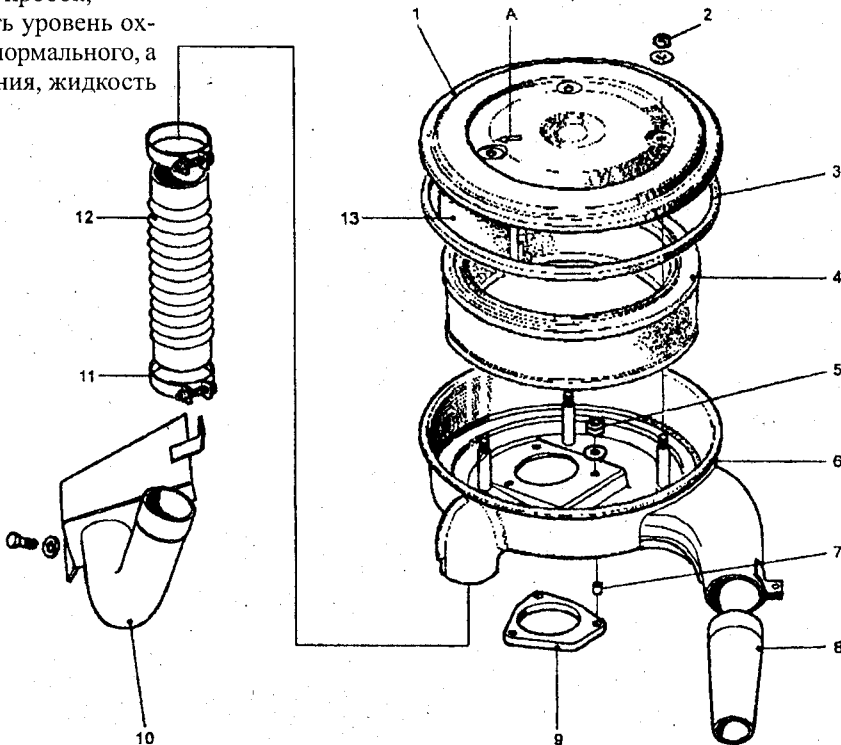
Воздушный фильтр и заборник теплого воздуха двигателя MeM3-246 (1.1 L): 1 – крышка; 2 – гайка крепления крышки; 3 – прокладка; 4 – фильтрующий элемент; 5 – гайка крепления корпуса; 6 – корпус; 7 – втулка; 8 – наставка; 9 – прокладка; 10 – заборник воздуха; 11 – хомут; 12 – шланг подвода воздуха; 13 – перегородка
